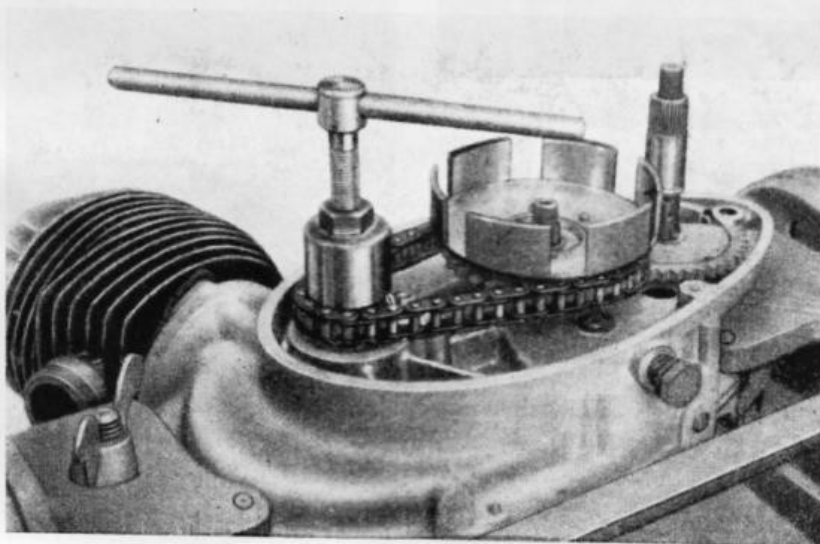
Odkręcanie nakrętki z lewego czopu wału korbowego
